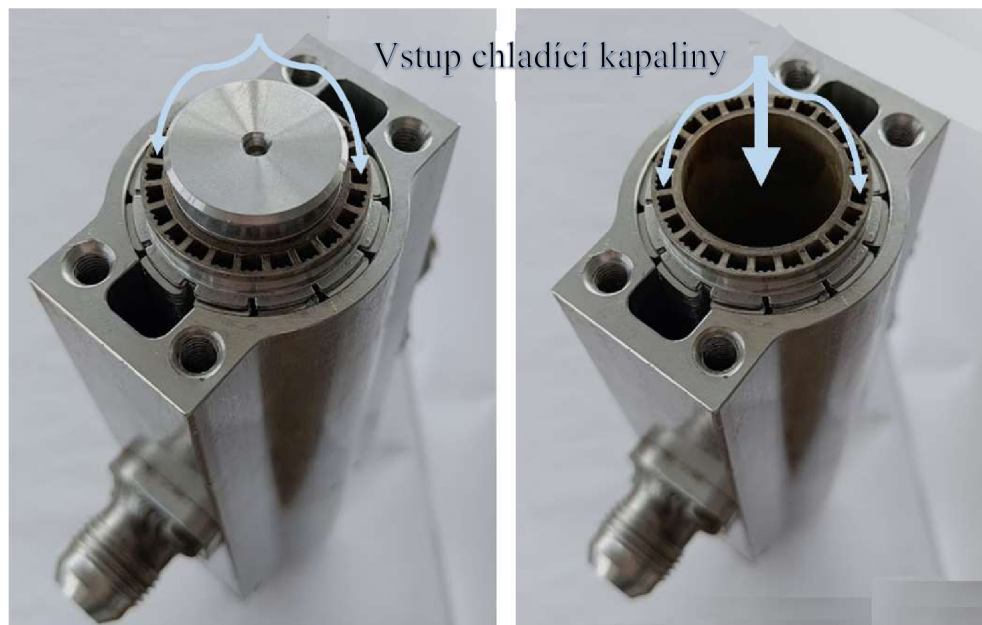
Hlavní komponenty olejového chladiče pro závodní automobil.
